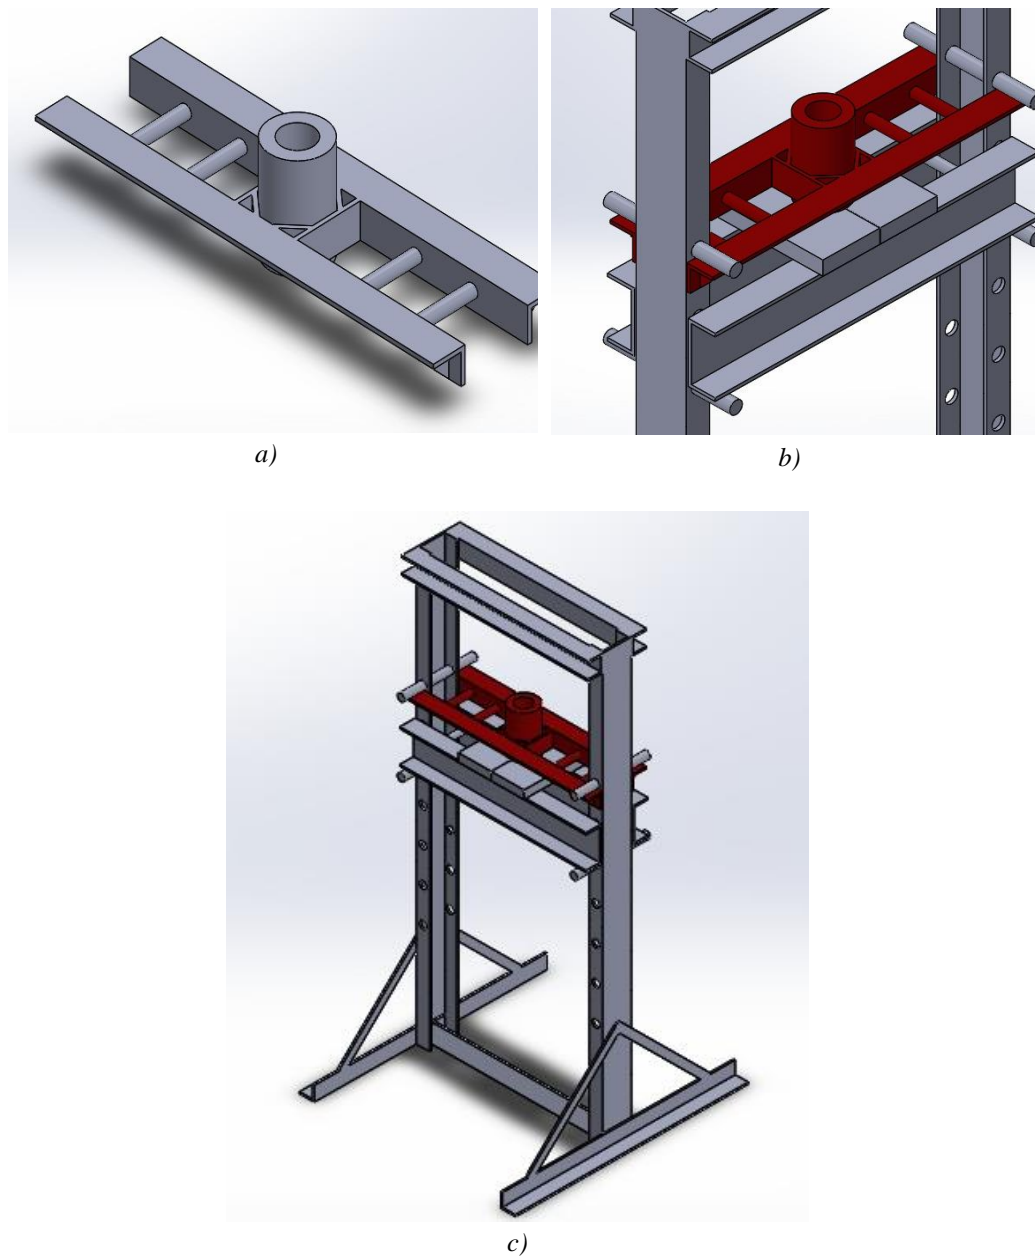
Ensamble removible entre la prensa hidráulica y el molde para briquetas. a) Se muestra el conjunto del molde, b) Conexión entre el molde y la prensa hidráulica, revelando los detalles principales sobre su montaje y sus apoyos, c) Montaje del molde en la prensa hidráulica desde una perspectiva general. Fuente: Elaboración propia.
